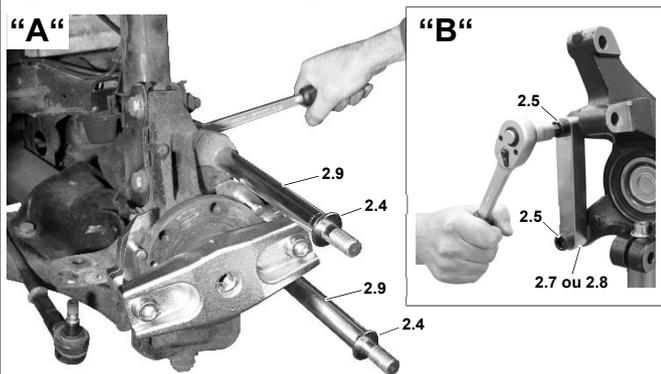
Monter la plaque de base sur les barres d'appui.
